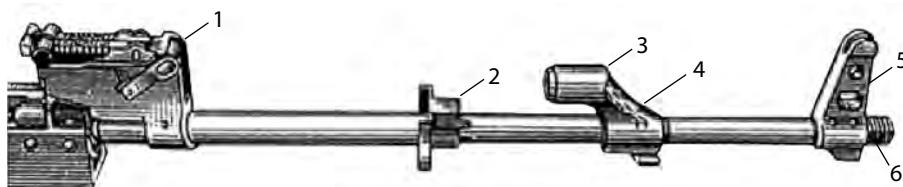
Ствол: 1 — колодка прицела; 2 — соединительная муфта; 3 — газовая камера; 4 — газоотводное отверстие; 5 — основание мушки; 6 — резьба
